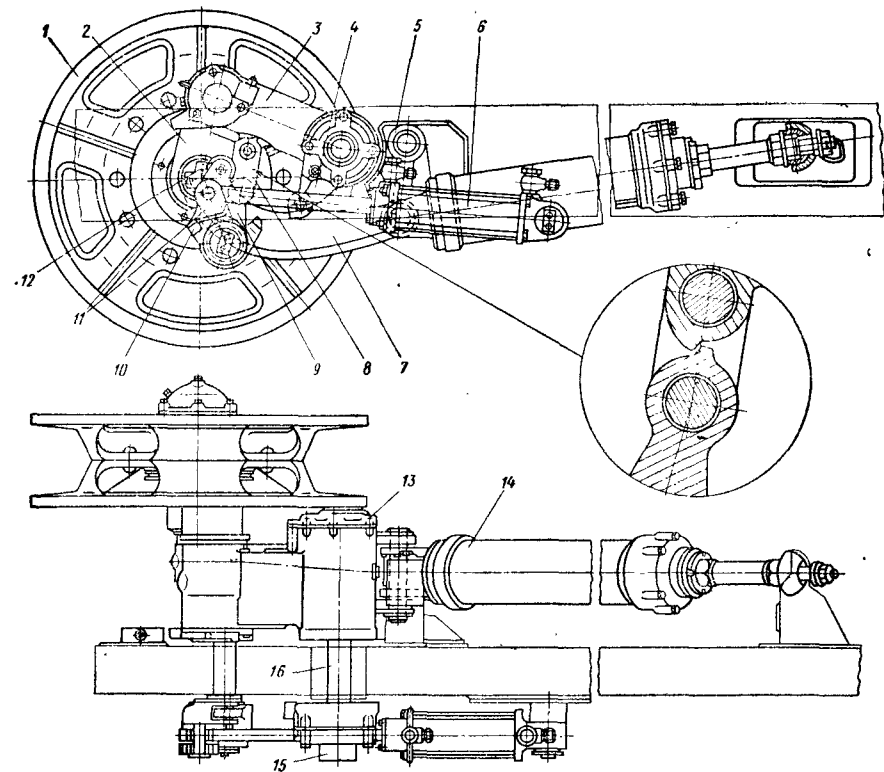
Кривошипно-балансирное натяжное приспособление трактора ДТ-75Б:
